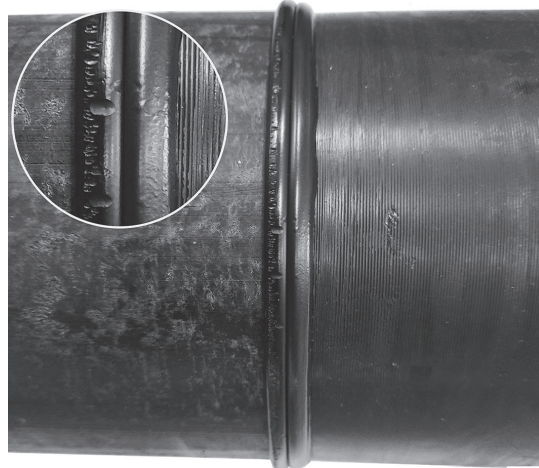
Валики грата сварного шва, полученного путем сварки труб из ПВП (слева) и ПЭ 100 (справа).
